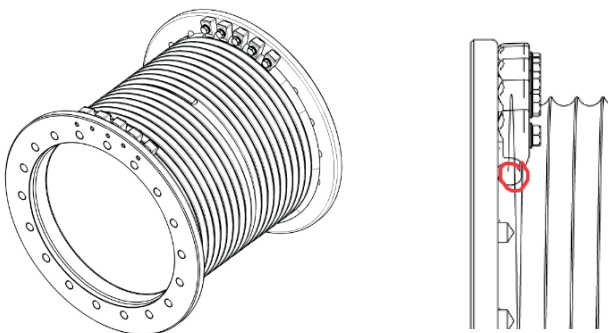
Coloque o cabo dentro da flange do tambor, garanta a posição correta das braçadeiras e aperte os parafusos com o torque fixo.
